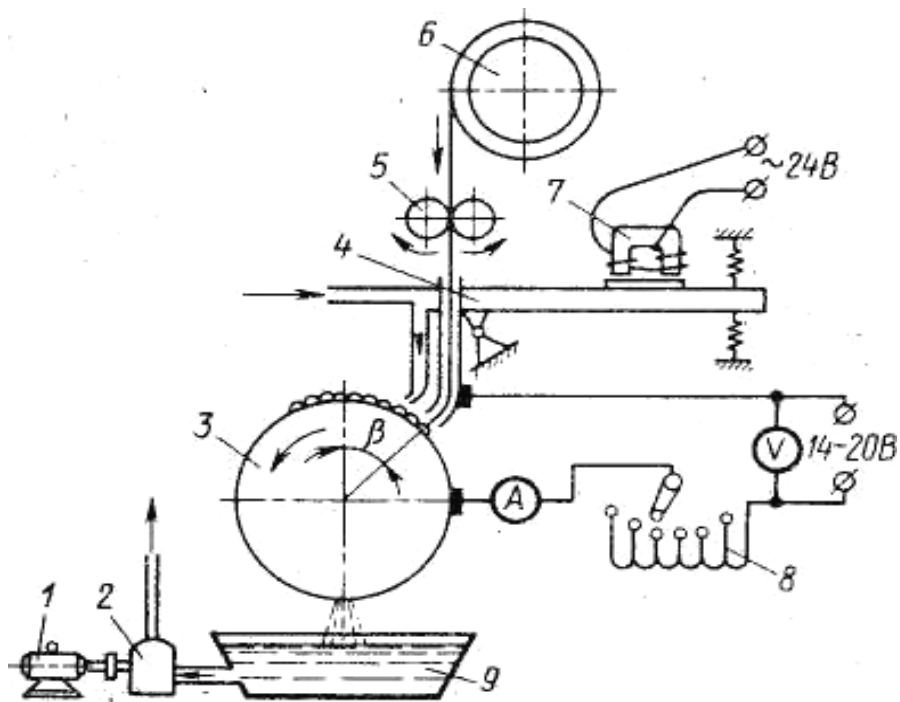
Схема установки для автоматичного вібродугового наплавлення: 1 — електродвигун; 2 — насос; 3 — деталь; 4 — вібрируючий мундштук; 5 — механізм подачі дроту; 6 — касета; 7 — вібратор; 8 — індуктивний опір; 9 — бак
